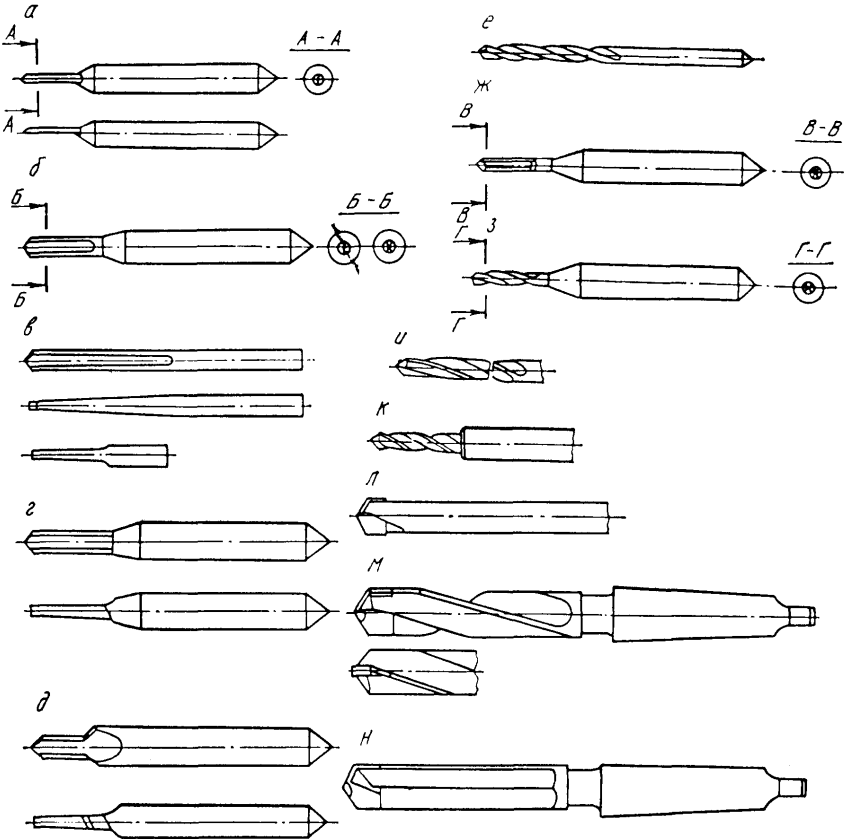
Типы мелкогабаритных быстрорежущих (а-з) и твердосплавных (и-н) сверл
